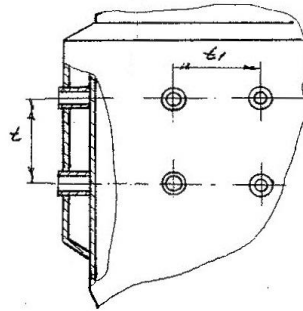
Сопряжение рубашки с корпусом анкерными трубами
